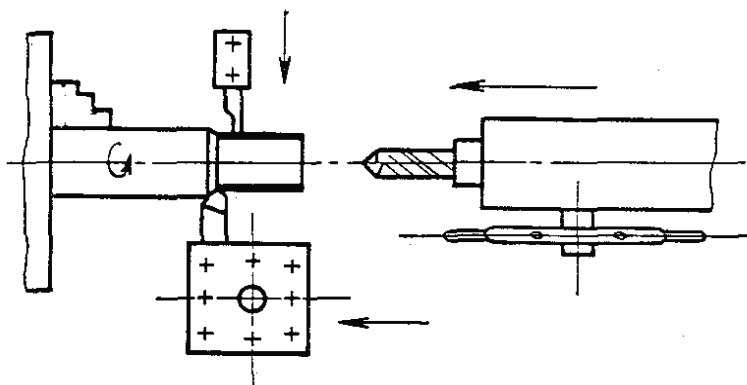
Схема обработки на токарно-сверлильно-отрезном станке
